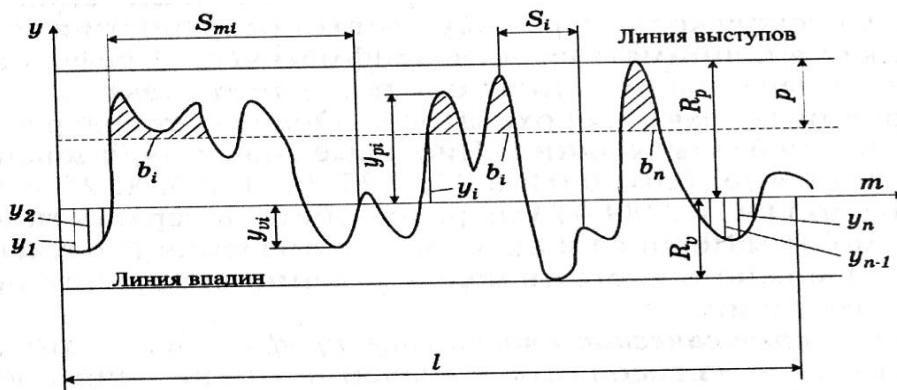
Профилограмма и основные параметры шероховатости поверхности
